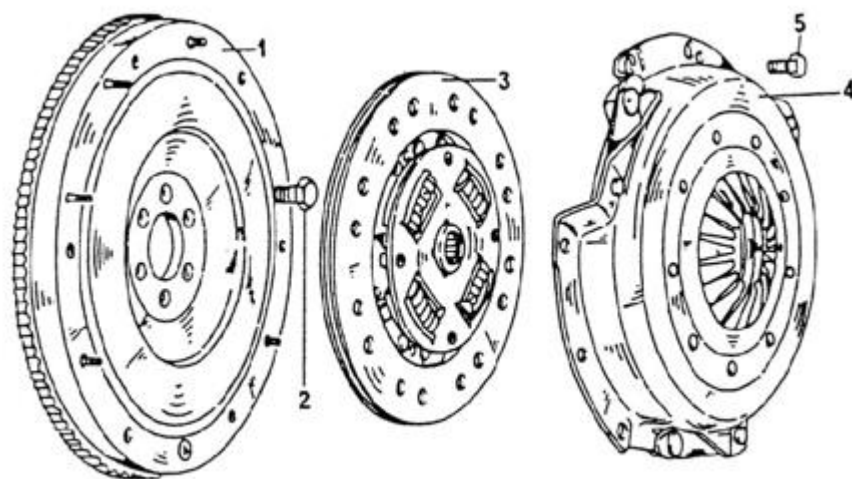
Однодисковое сцепление: 1 – маховик; 2 – винт крепления маховика; 3 – ведомый диск; 4 – корпус сцепления; 5 – крепежный винт
